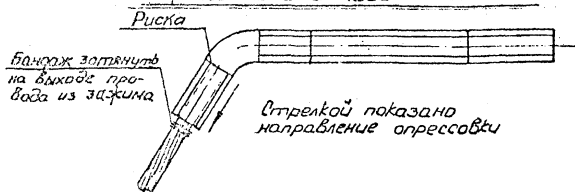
Корпус натяжного зажима типа НАСУС по черт. МО СКБ
